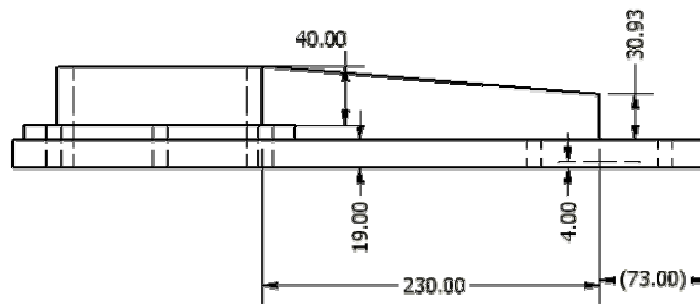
16. Detalle que muestra las dimensiones de la aleta refuerzo la placa. Fuente: Los Autores.
